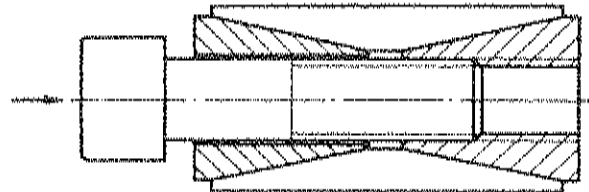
Entspannt der hintere Druckring nicht selbsttätig, so werden die Schrauben um einige Gänge herausgedreht. Nach einigen leichten Schlägen gegen die Schraubenköpfe springt der Druckring nach hinten.
